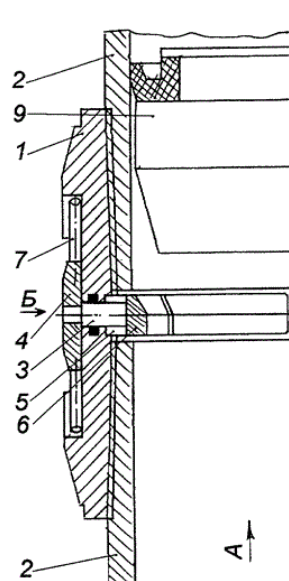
Центратор гидравлический: 1 – корпус; 2 – обсадные трубы; 3 – шток; 4 – опора; 5 – кольцевая канавка; 6 – сектора; 7 – упругие стержни; 8 – фигурные вкладки; 9 – распорный конус
